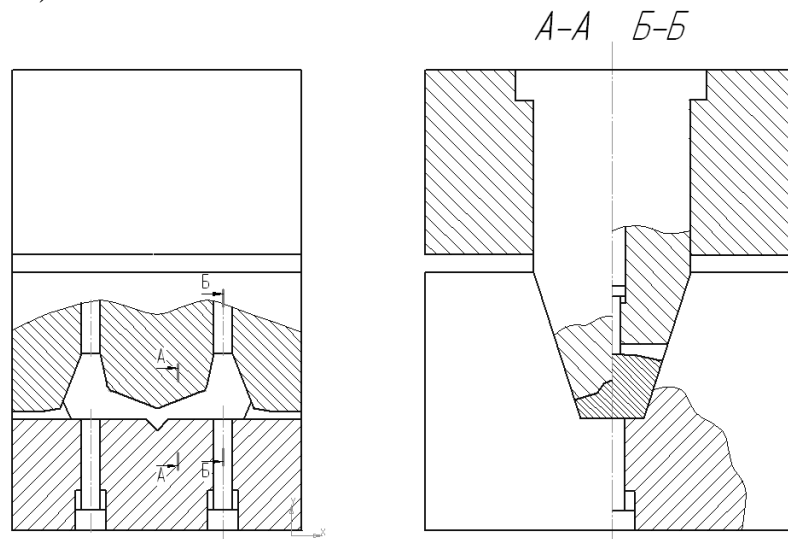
Схема перетискного рівчака КГШП для виготовлення сухаря
